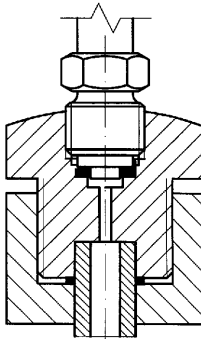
Zylindrische Gewinde, Abdichtung mit Dichtung an Dichtfläche
